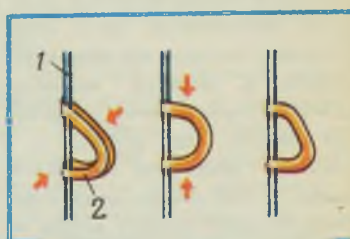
Изготовление скобы из кружка мягкой латуни:
